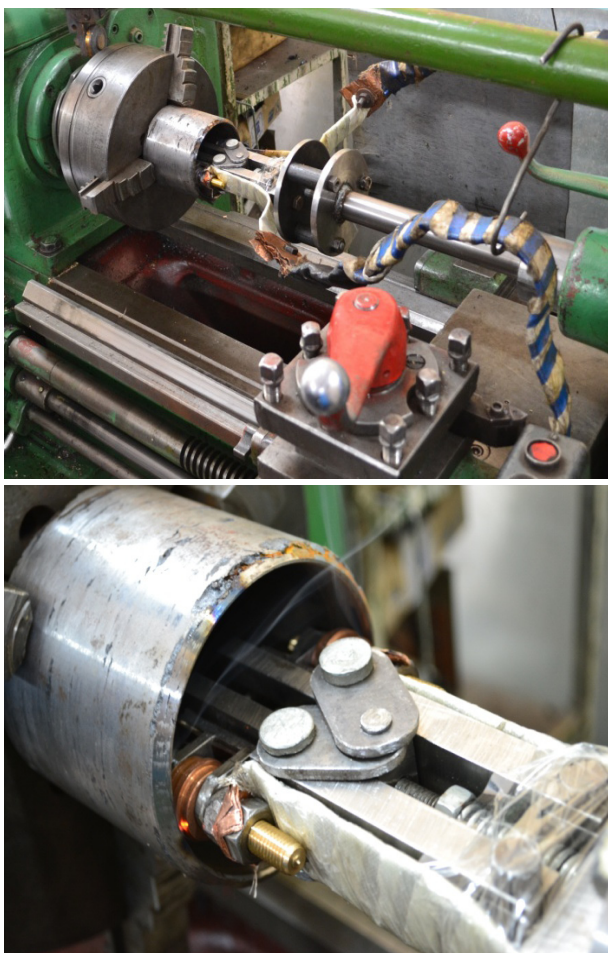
Державка для ЭМЗ гладких цилиндрических отверстий
